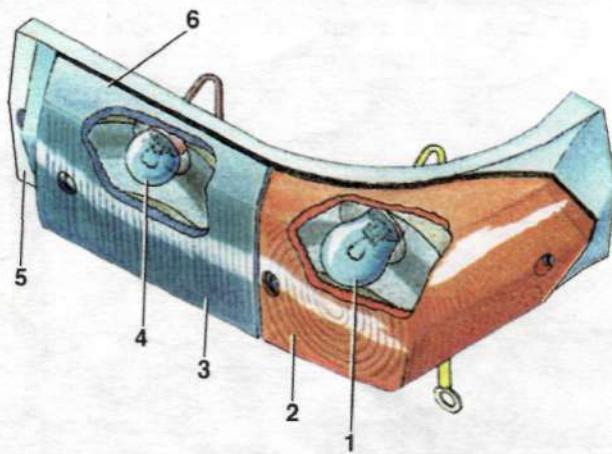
Подфарник. 1. Лампа указателя поворота. 2. Рассеиватель указателя поворота. 3. Рассеиватель габаритного света. 4. Лампа габаритного света. 5. Корпус. 6. Прокладка.
